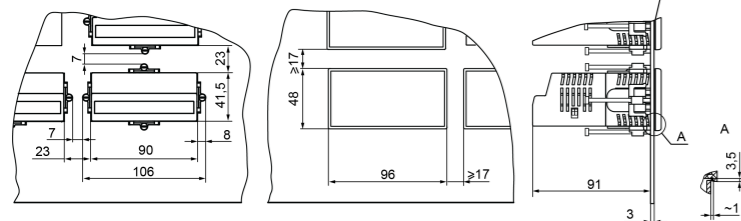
Прибор в корпусе Щ2, установленный в щит толщиной 3 мм
